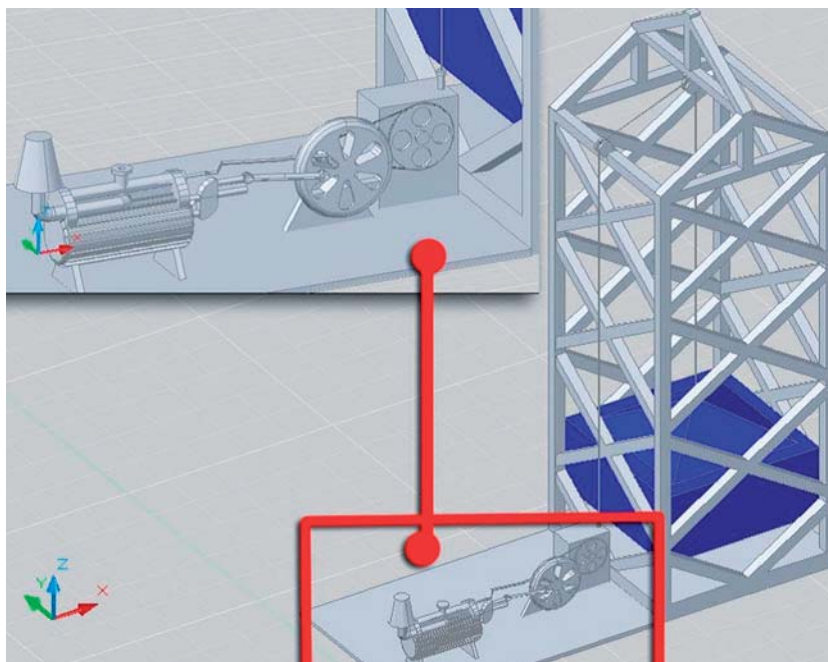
Трехмерный вид конструкции накопителя избыточного давления
